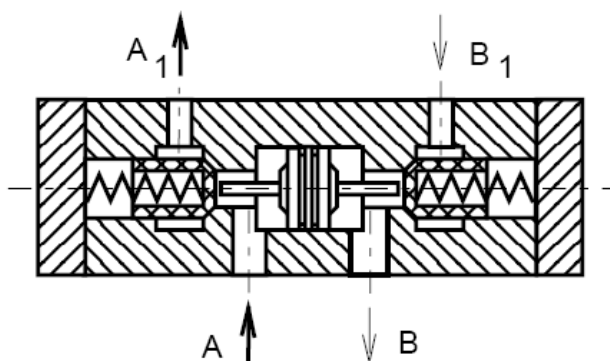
Jednosměrný ventil s kuželkou [2]
